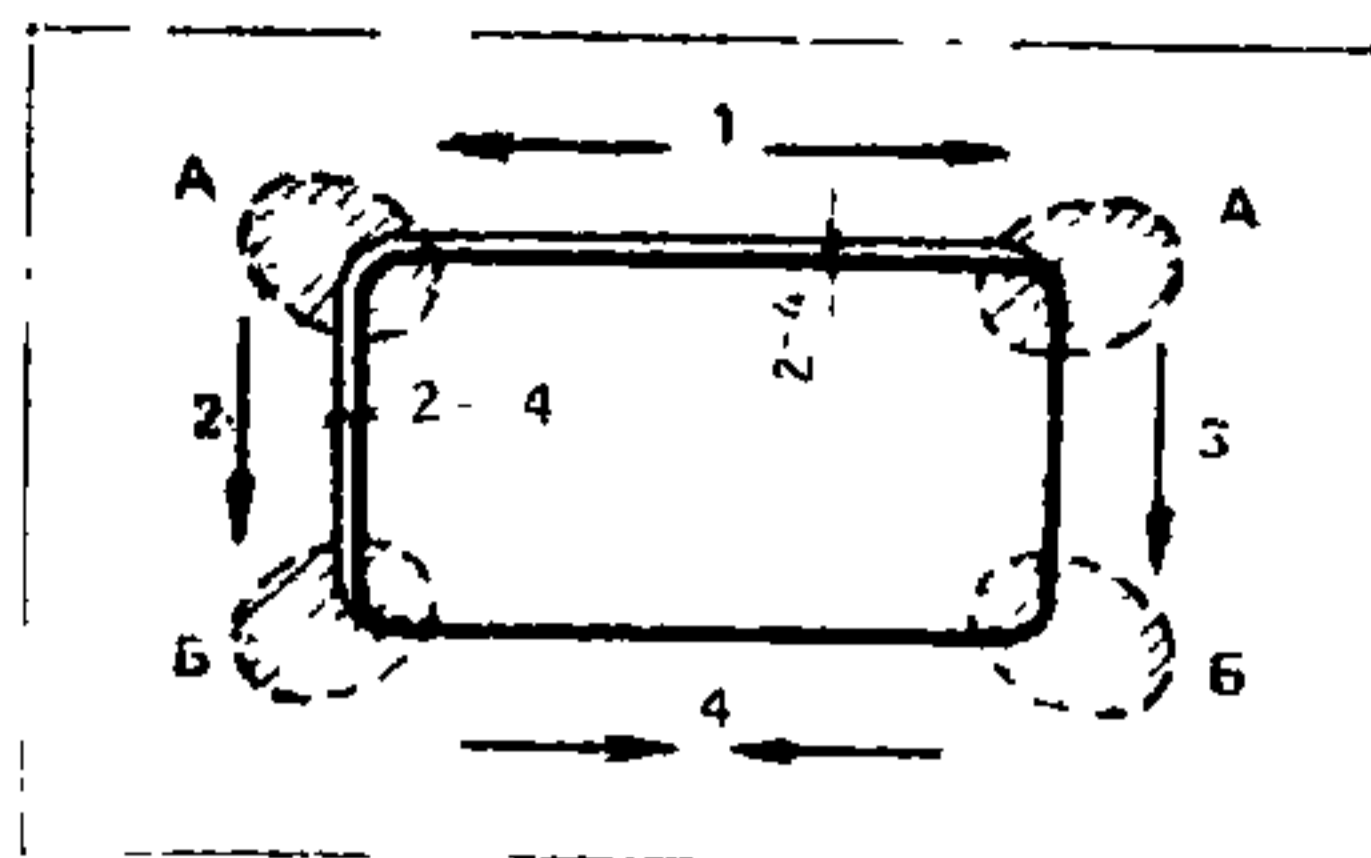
Участки подогрева и последовательность сварки вставки
